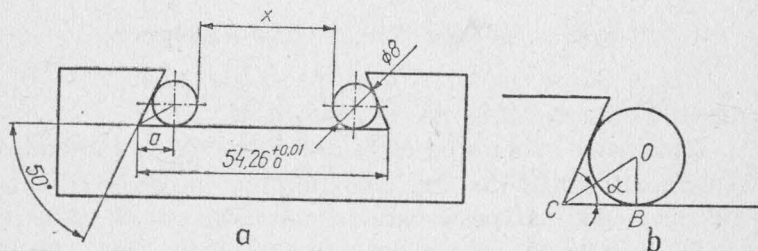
Măsurarea dimensiunii cozii de rîndunică:
